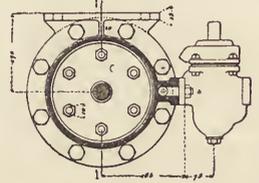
Horizontalschnitt und Grundriss.
